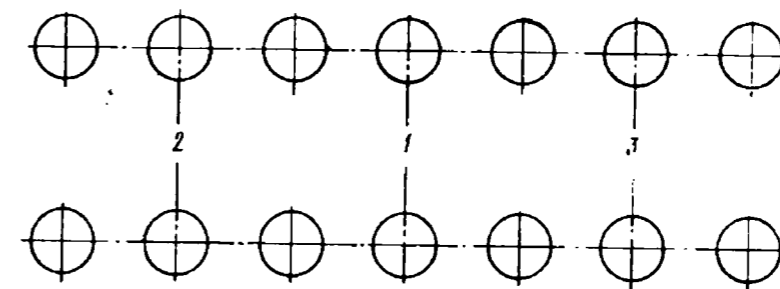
Последовательность затяжки гаек крепления блока при обжатии деталей газового стыка
